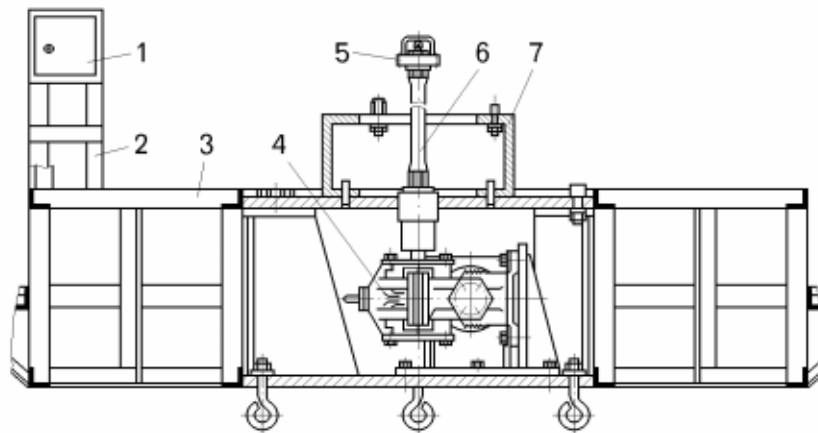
Стенд для регулировки конических подшипников:
